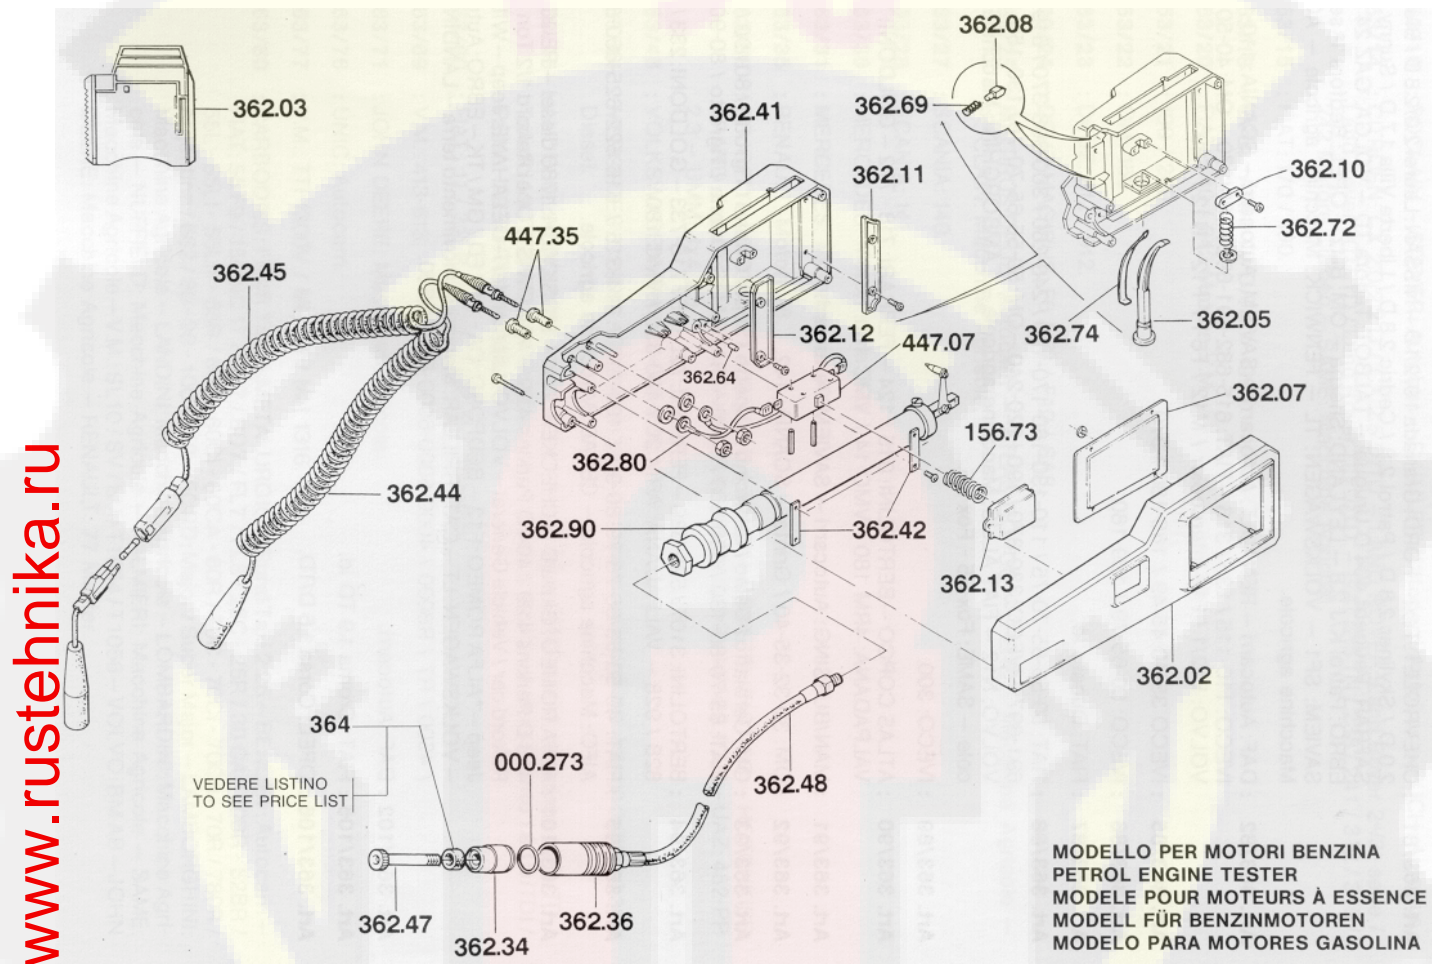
Детализовка элементов компрессографа для бензиновых двигателей №362
